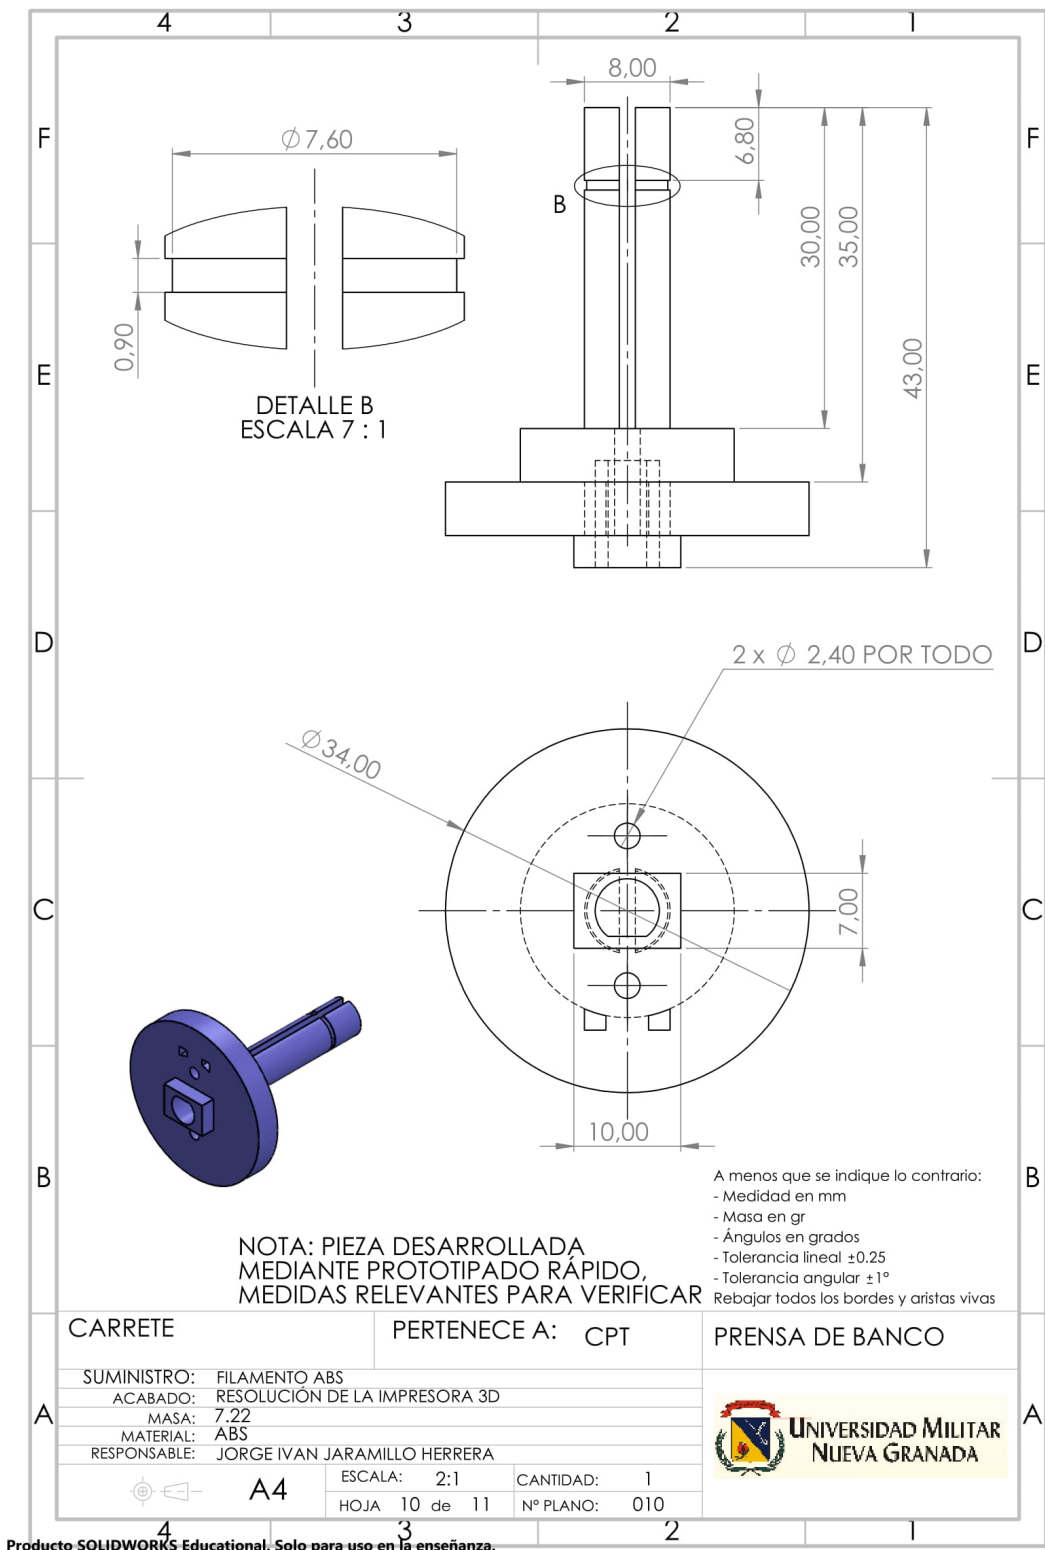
Plano 010, de la pieza "Carrete". Modelo CAD y plano elaborado por el autor mediante la herramienta de pieza y dibujo de "Solidworks".
